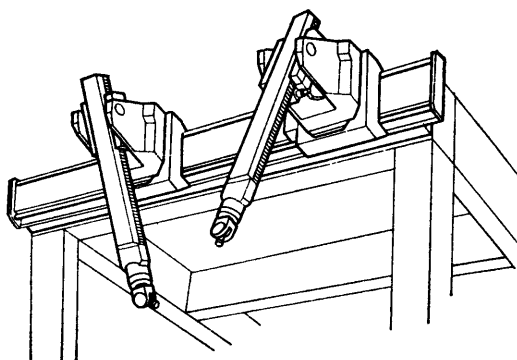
Тельферные роботы с цилиндрической системой координат для сварки дна
